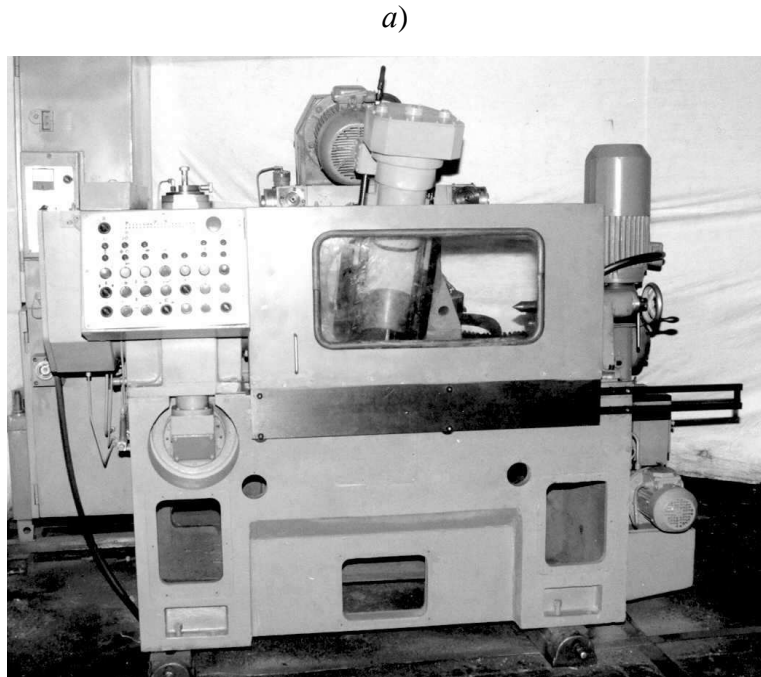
Широкоуниверсальный зубошлицефрезерный станок модели ВС-50:
